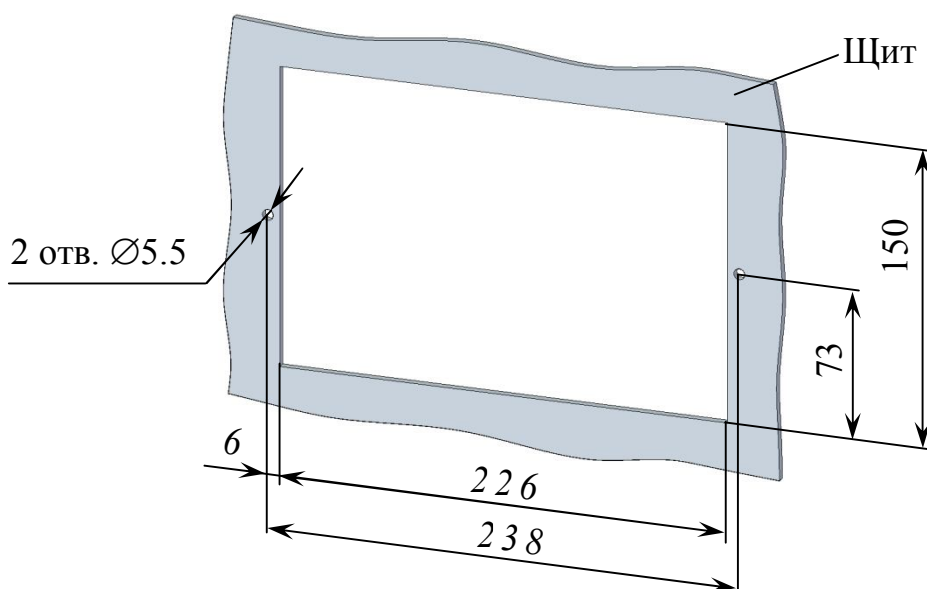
Разметка отверстий в щите для крепления блока преобразовательного щитового исполнения
